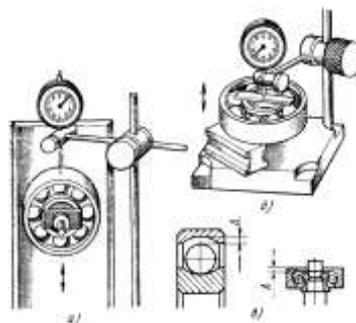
Индикаторное приспособление для измерения осевого разбега в подшипниках
